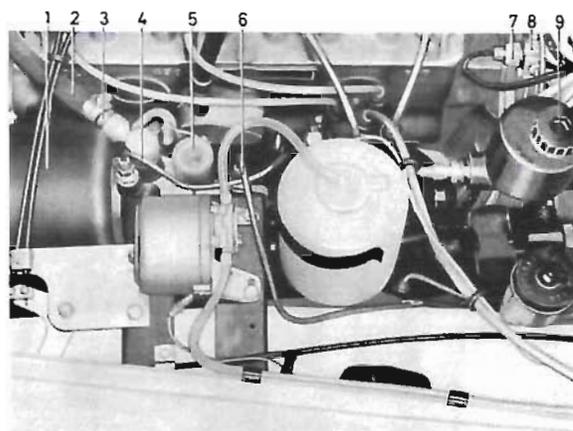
Bremsteile im Motorraum, P 1800 (ab Fahrgestell-Nr. 7000)
